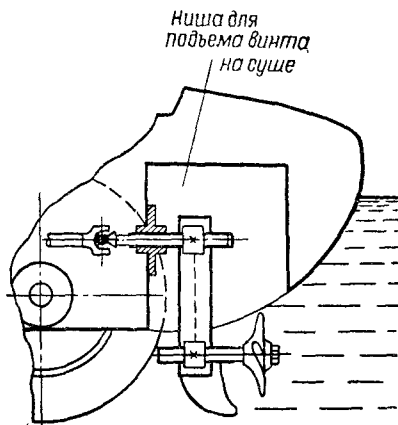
Схема размещения убирающегося гребного винта в нише плавающего колесного автомобиля
